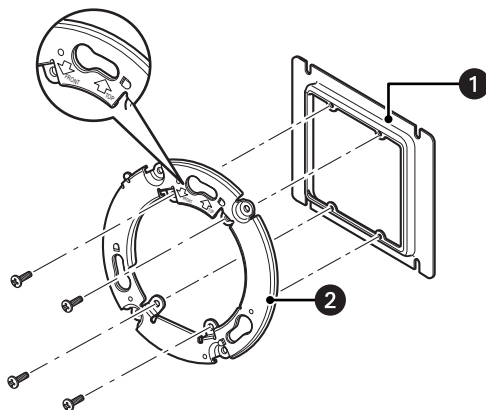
Установка крепления камеры на сдвоенную клеммную коробку
